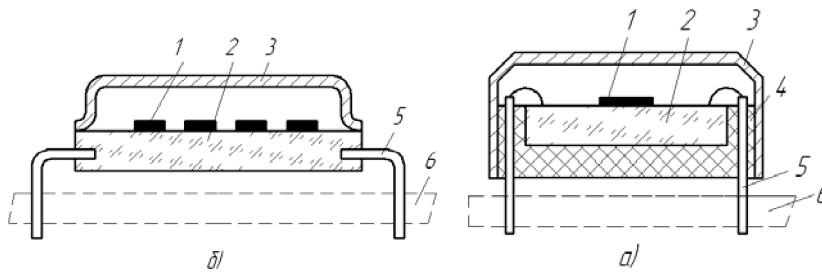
Металлополимерный (а) и металлокерамический (б) корпуса
